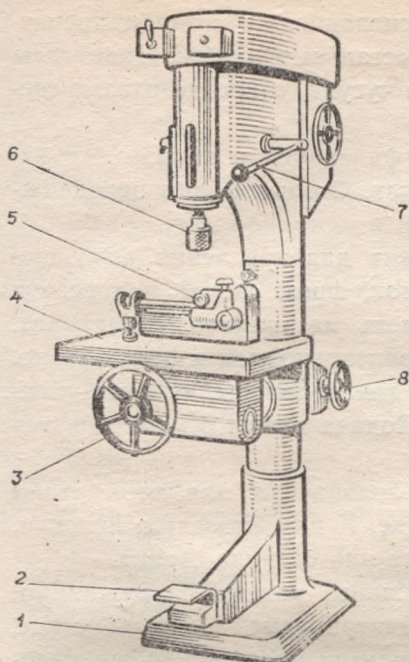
Вертикальный сверлильно-пазовальный станок:
